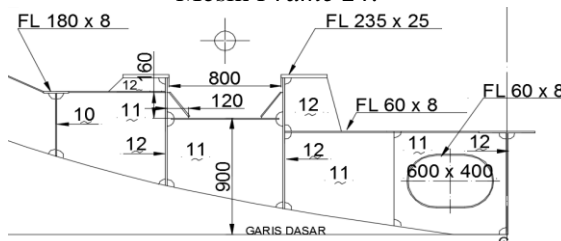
Konstruksi Melintang Pondasi Mesin Frame 14.
